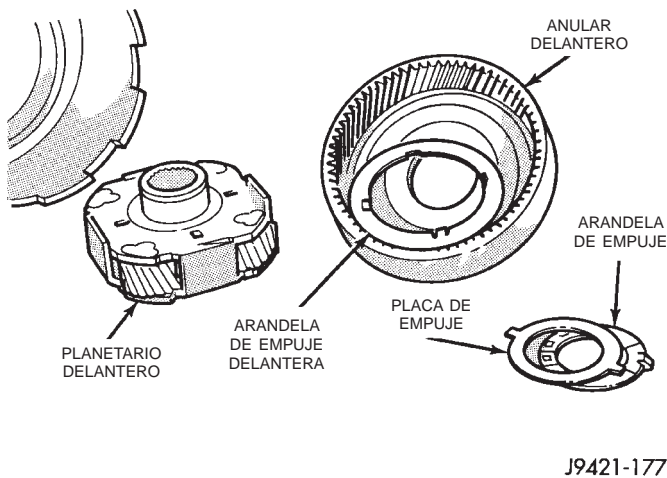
Desensamblaje del engranaje planetario y anular delantero
